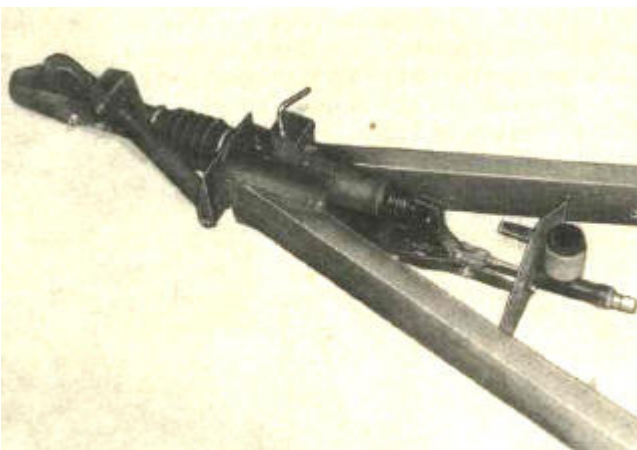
In eine V-Gabel eingeschweißtes Auflaufschubstück mit angeschraubter Kuglkupplung
